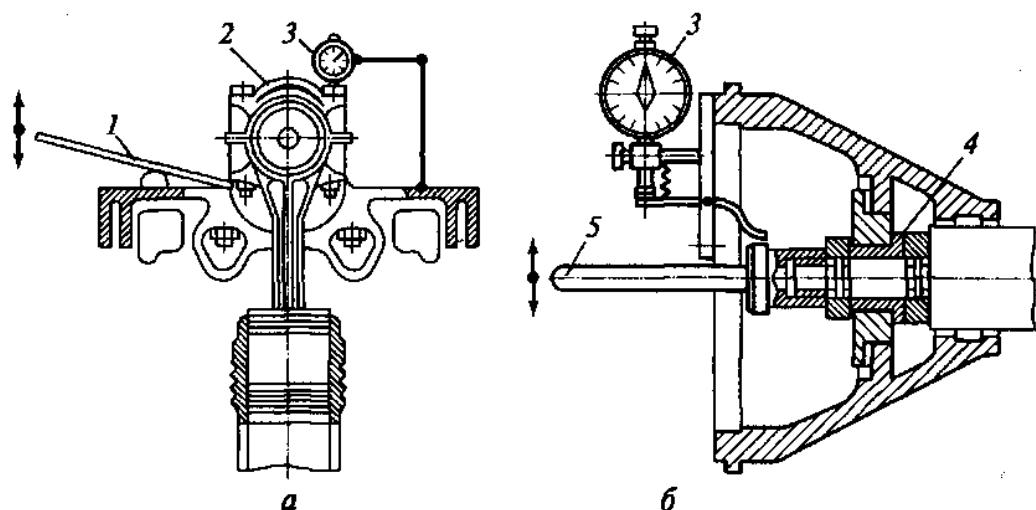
Схема измерения зазора «на масло» в подшипниках скольжения индикаторным приспособлением:
